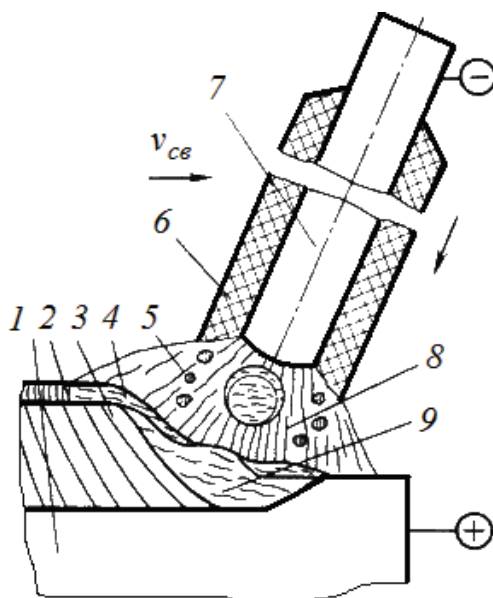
Схема дуговой сварки: 1 — деталь; 2 — шлаковая корка;
